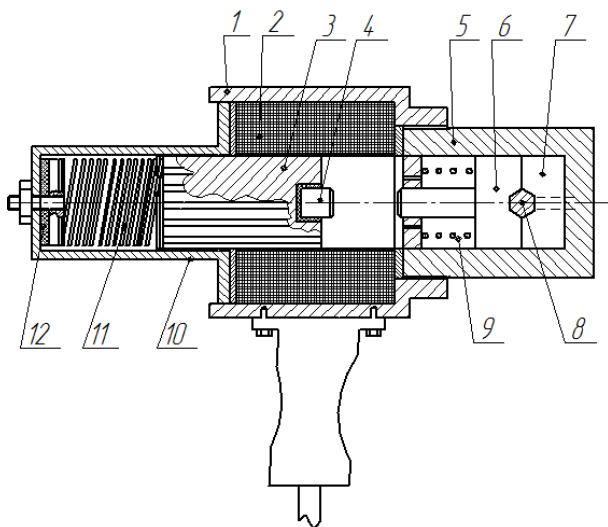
Схема низкочастотной ручной ударной машины с энергией удара 40-50 Дж: 1 – корпус; 2 – электромагнитная катушка; 3 – боек; 4 – ударник; 5 – матрицедержатель; 6 – пуансон; 7 – матрица; 8 – обрабатываемое изделие; 9 – поджимающая пружина; 10 – корпус возвратного механизма; 11 – возвратная пружина; 12 – вибродемпфер
